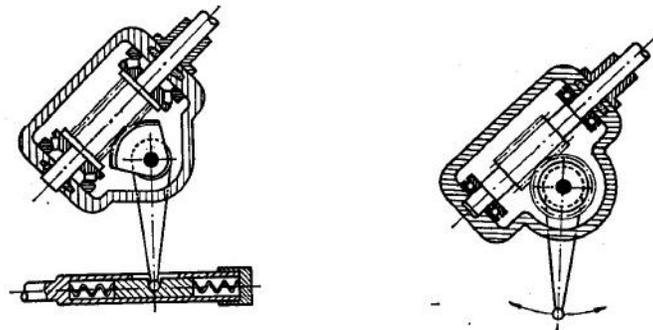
Tornillo sin fin y tuerca dentada y sector dentado.
